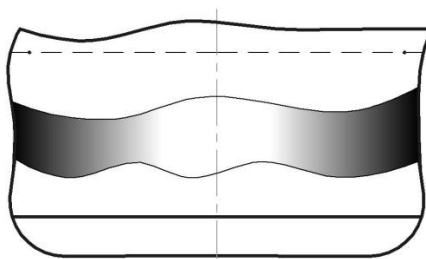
Форма поверхности среза вырубленной детали при малом зазоре.
